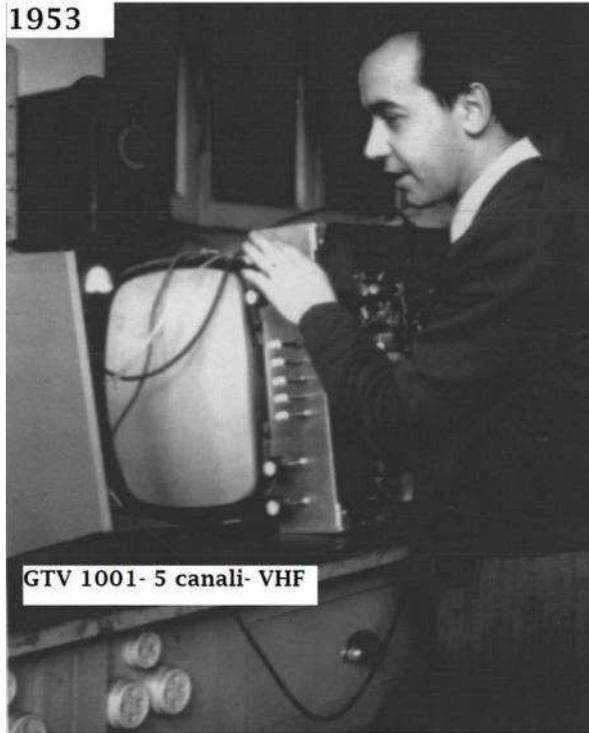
Una fase parte di montaggio del TV Geloso.
